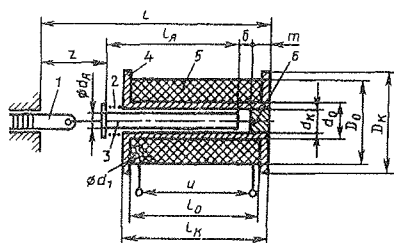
Электромагнит: 1 – рейка топливного насоса; 2 – пружина; 3 – якорь; 4 – корпус; 5 – обмотка
